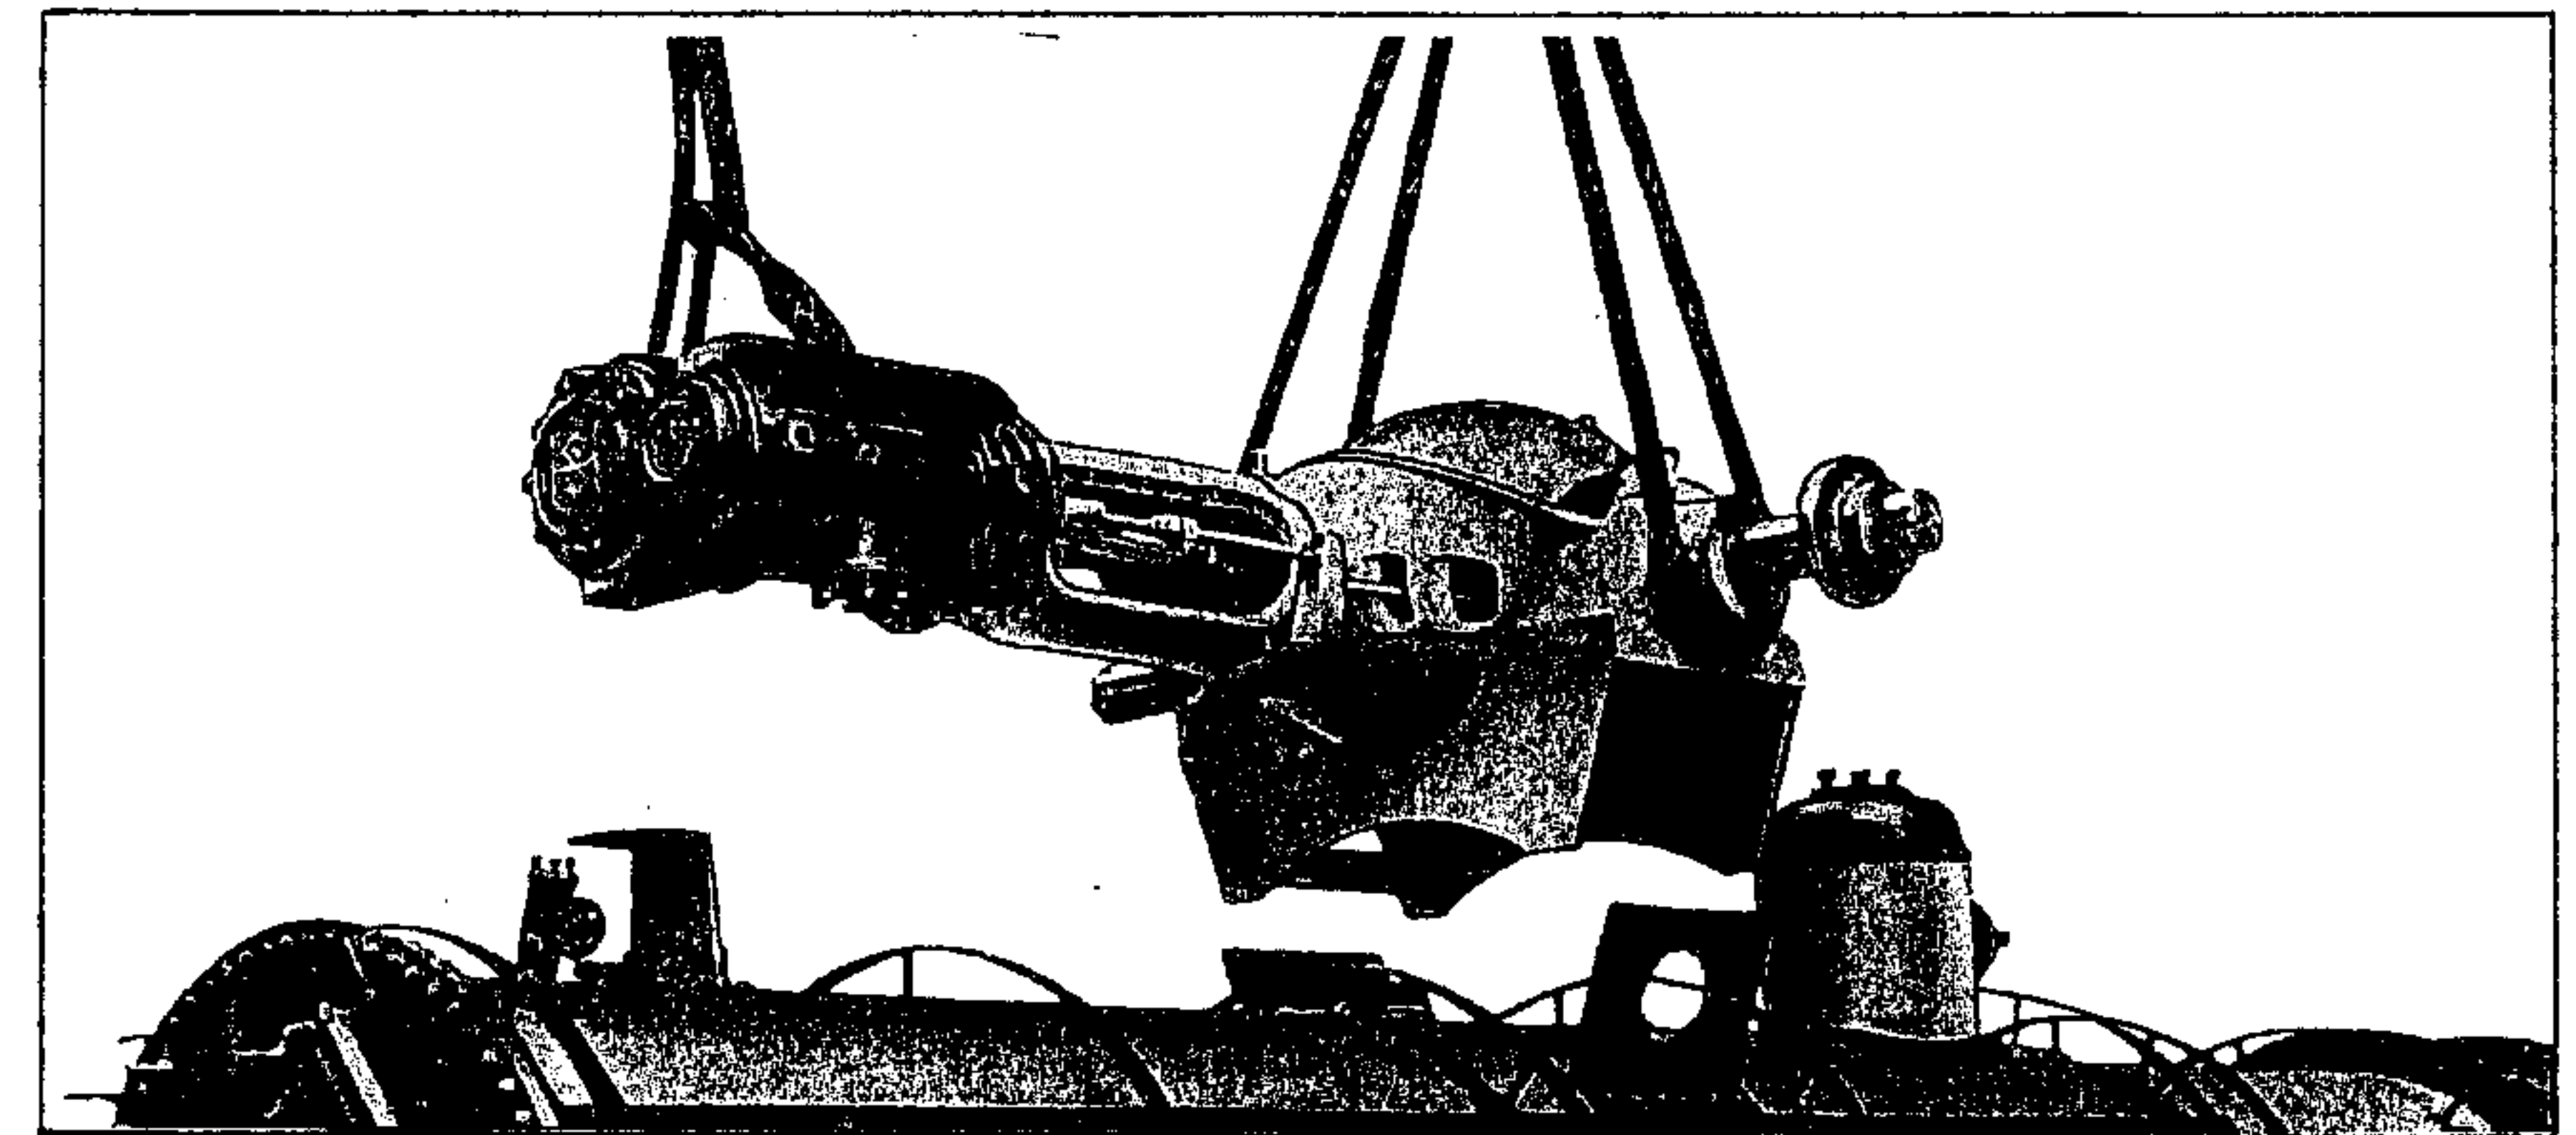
/2: Integriertes Lager- und Führungsteil einer Halblokomobile Typ H 7 bei der Montage (Henschel & Sohn, um 1920)
